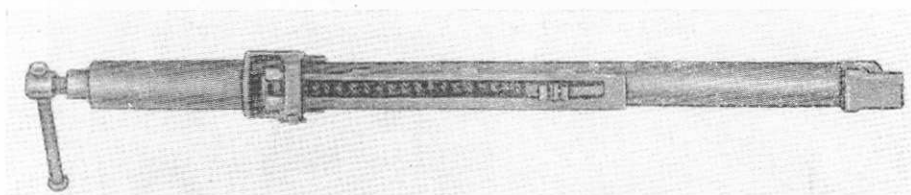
Присоединение к возвратному механизму приспособления для его разборки
